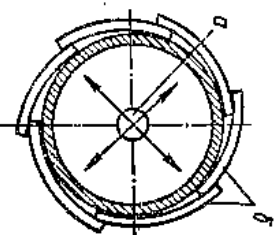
Схема панорамного просвечивания сварных стыков трубопроводов с расположением радиоактивного источника излучения в центре трубы:
